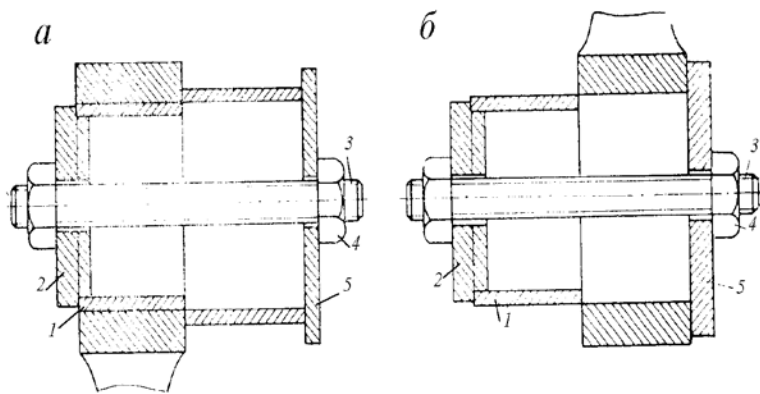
Приспособление для выпрессовки (а) и запрессовки (б) втулок крейцкопфной головки шатуна: 1 – втулка; 2 – диск; 3 – болт; 4 – гайка; 5 – оправка
